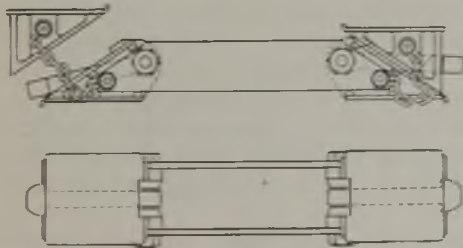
Cookson- oder Meco-Lösevorrichtung für Holzkasten.
